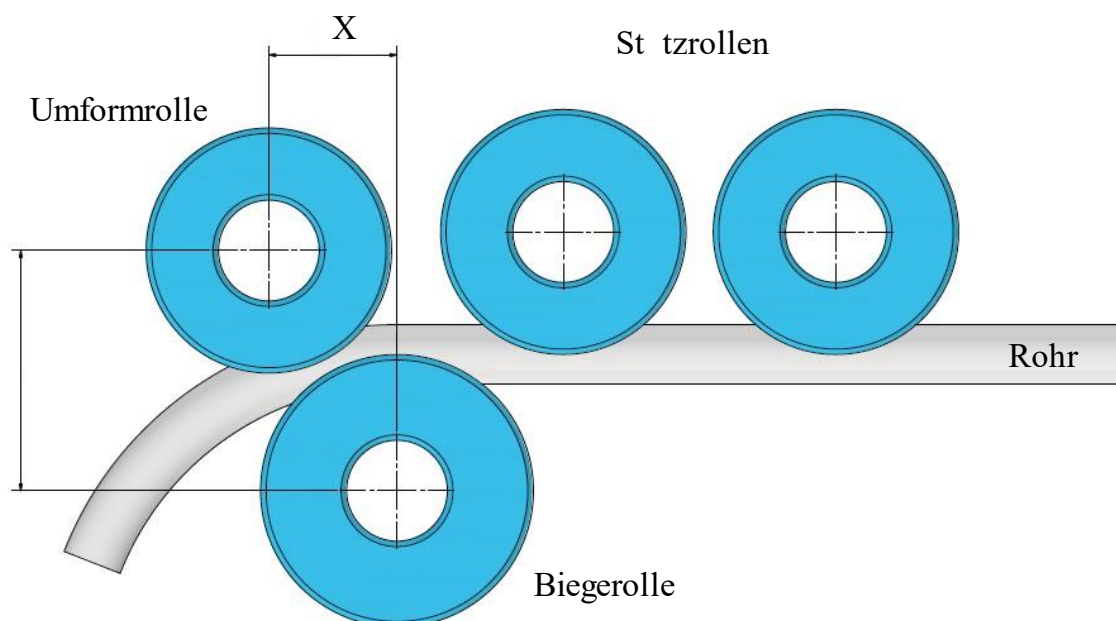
Schematischer Werkzeugaufbau für das Drei-Rollen-Schubbiegen
